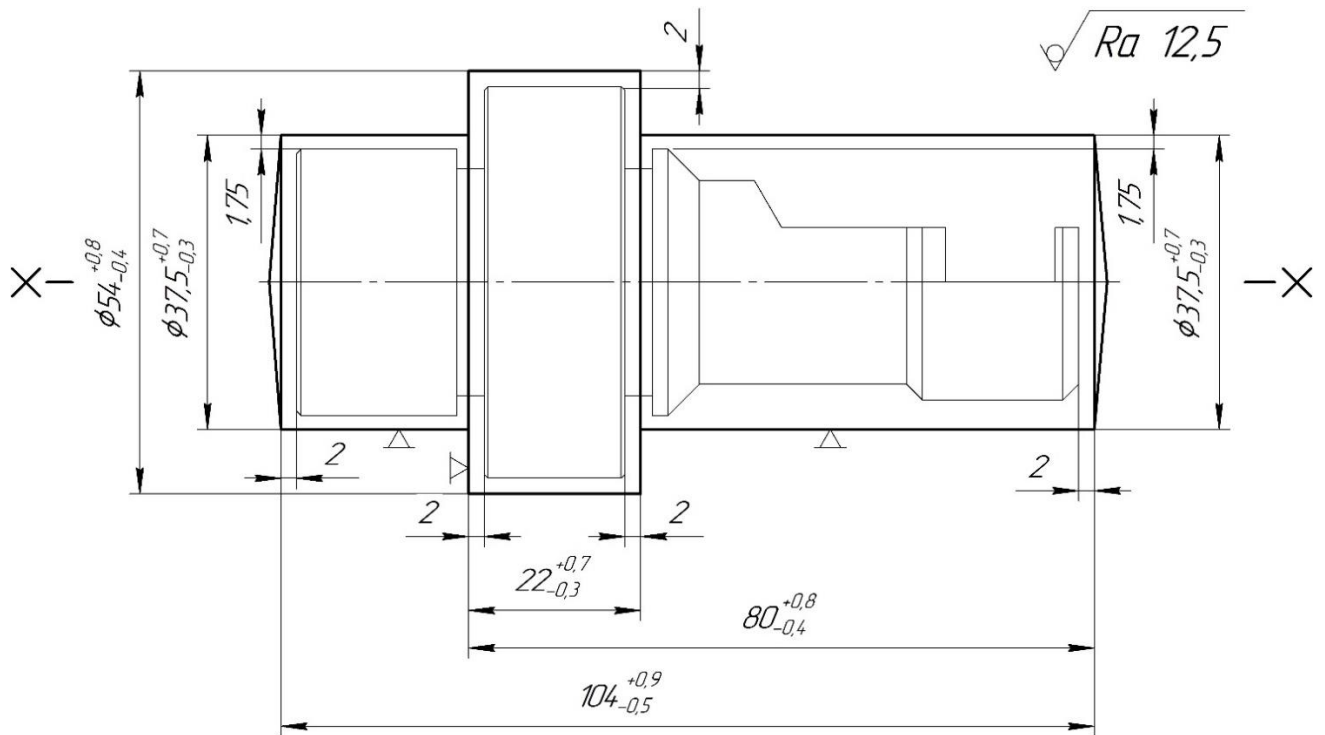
Ескіз заготовки виготовленої на КГШП
